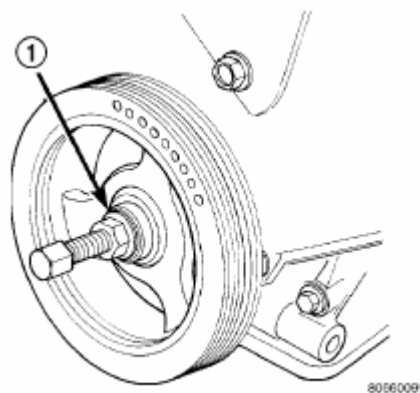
Установка гасителя вибрации коленчатого вала – типовая.
